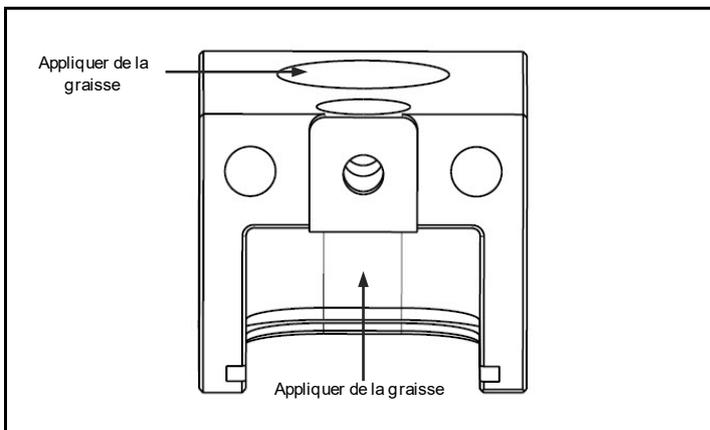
Préparer le logement de la boîte d'engrenages
